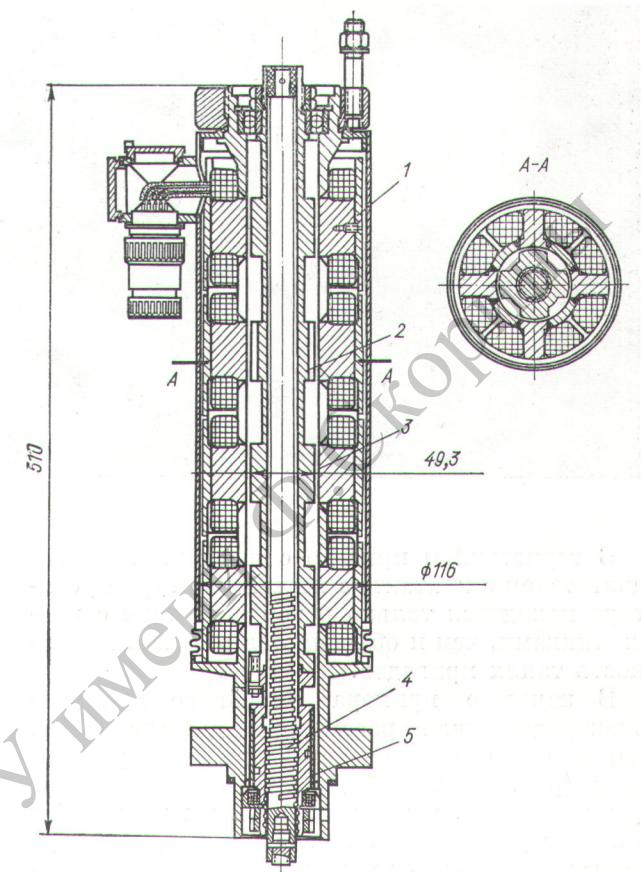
Общий вид привода компенсирующего стержня реактора СМ-2:
